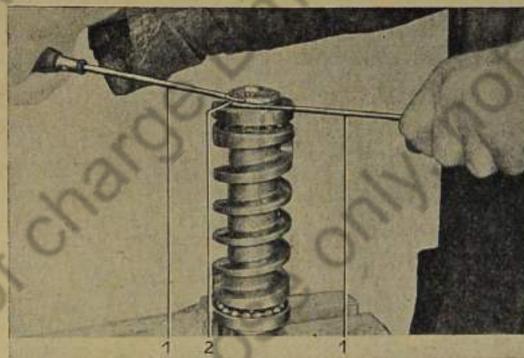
Sprengring aus der Lenkschnecke herausdrücken
